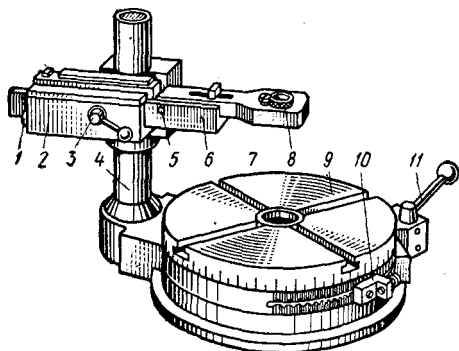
Универсально-наладочное приспособление к радиально-сверлильным станкам
